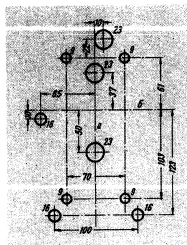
Сверление отверстий для установки на изоляционных плитах контакторов типа КП 523 и КП 533 с задним присоединением
